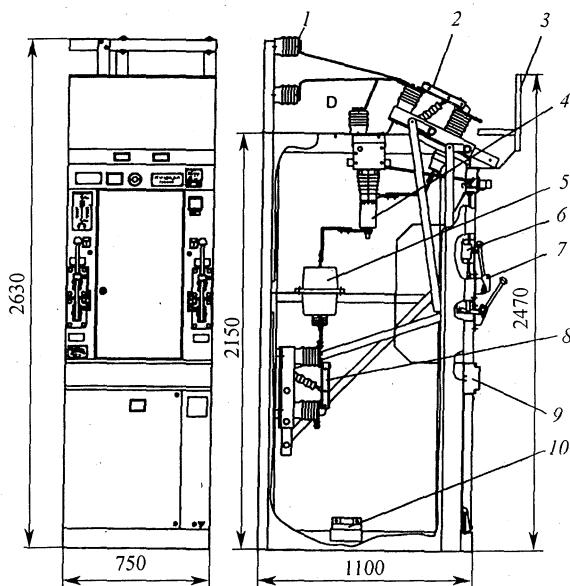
Камера КСО-298: 1 — сборные шины; 2 — разъединитель; 3 — защитный экран; 4 — выключатель; 5 — трансформаторы тока; 6 — блокиратор; 7 — приводы разъединителей; 8 — линейный разъединитель; 9 — клеммник; 10 — трансформатор тока нулевой последовательности
